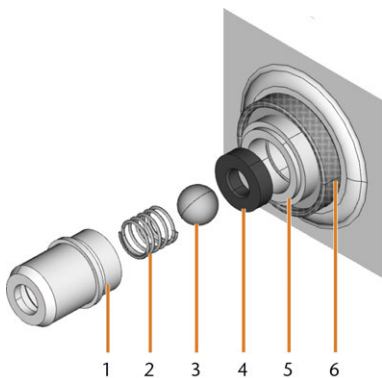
COMPONENTES DEL ENGANCHE DEL DEPÓSITO DE LÍQUIDO REFRIGERANTE
